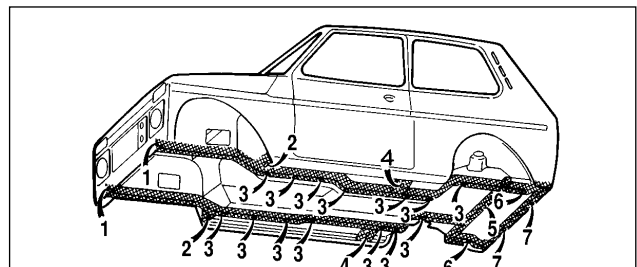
Cavités cachées (vue par dessous de la carrosserie):
